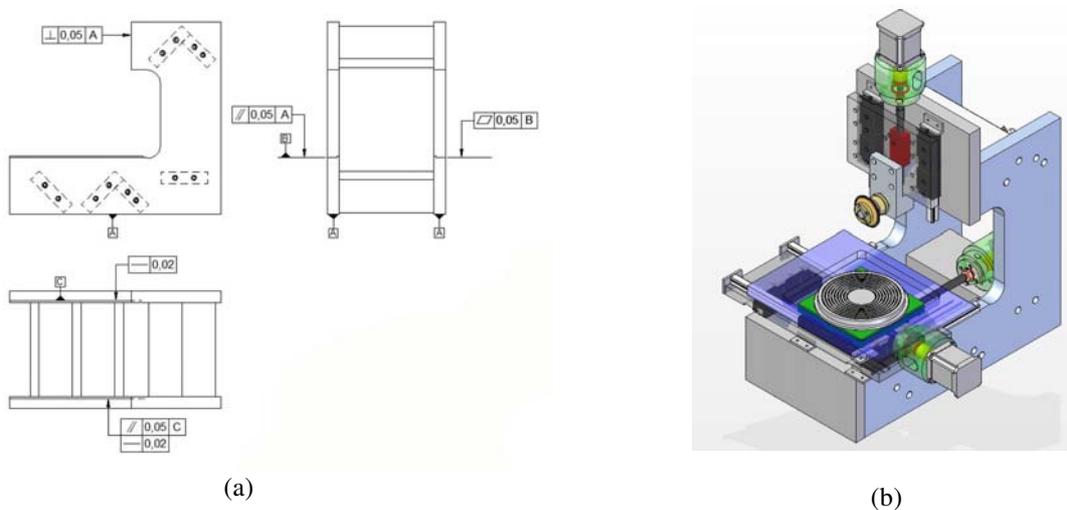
(a) – Tolerâncias da estrutura; (b) conjunto montado final: protótipo mini-máquina de corte.
